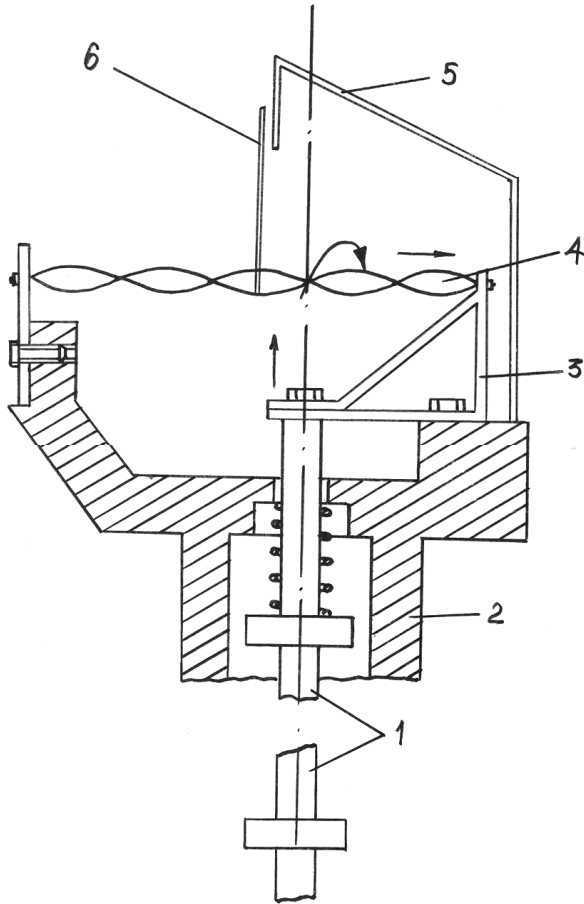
Принципова схема мікрометра: 1 – вимірювальний стержень; 2 – установча скоба; 3 – пружина плоска; 4 – пружина скручена; 5 – шкала; 6 – стрілка
